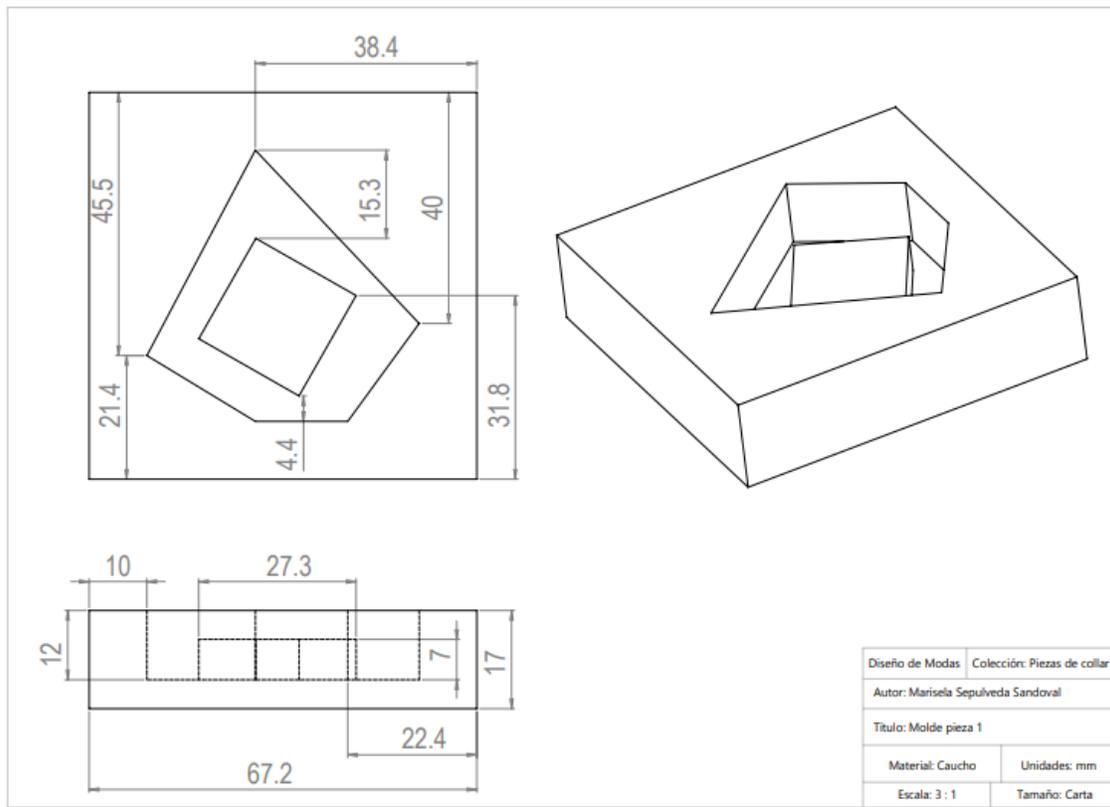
Dimensiones del contra-molde de caucho de la pieza 1.
